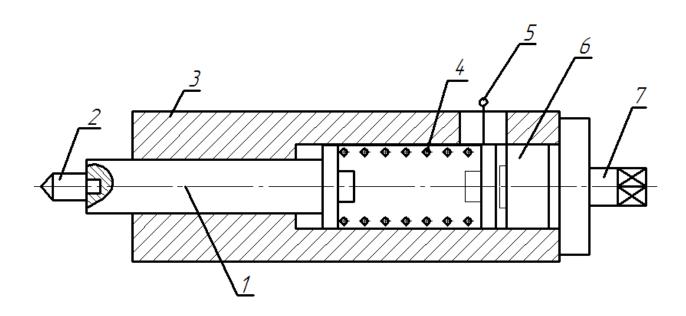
Приспособление для выглаживания рабочих поверхностей вала: 1-шток; 2-выглаживатель; 3- корпус; 4- силовая пружина; 5- индикатор силы выглаживателя; 6 –плунжер; 7 – винт регулировочный.
